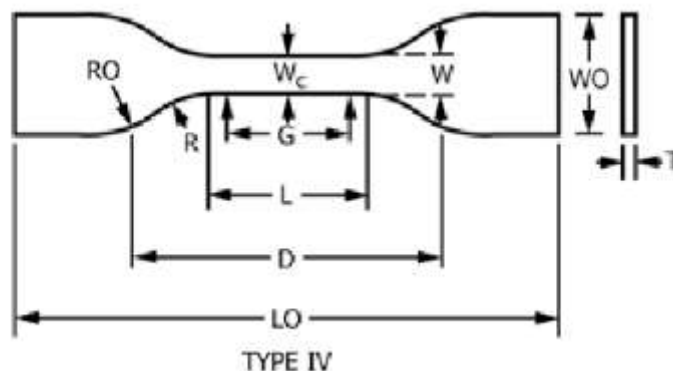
Dimensions d'éprouvette dogbone standardisée
